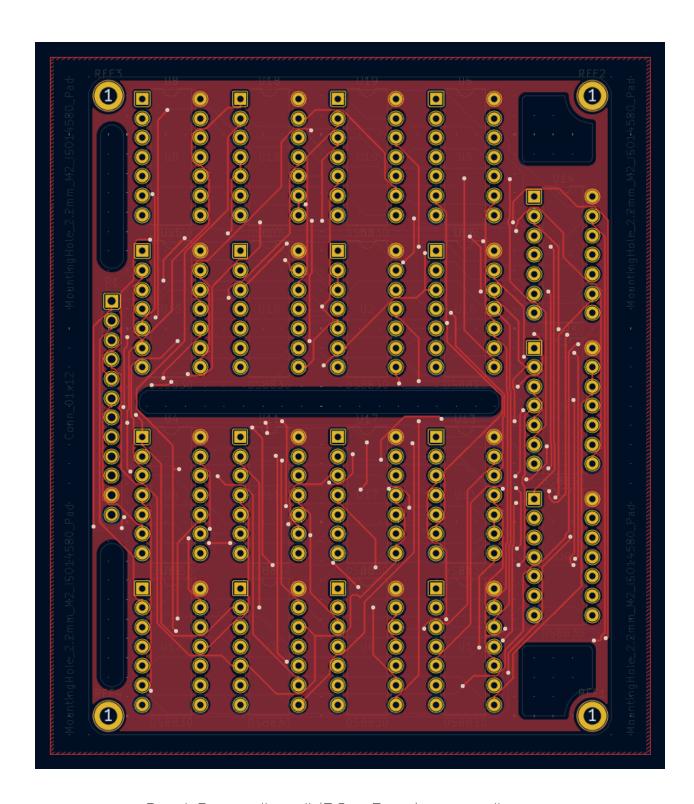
Верхний слой (F.Cu - Front) печатной платы
